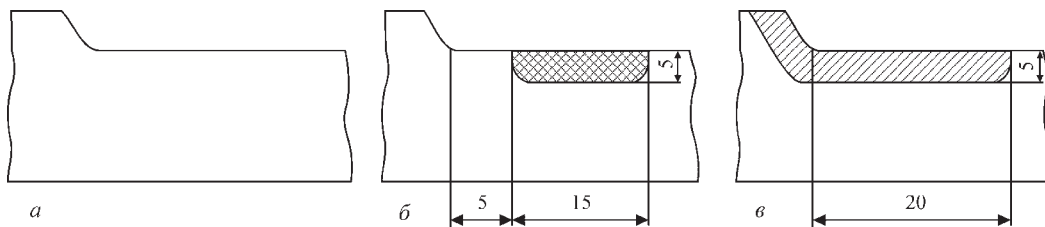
Схемы выполнения восстановительной наплавки образцов для испытаний на усталость: исходный (а); с разделкой под наплавку по схеме 1 (б) и с разделкой под наплавку по схеме 2 (в)
